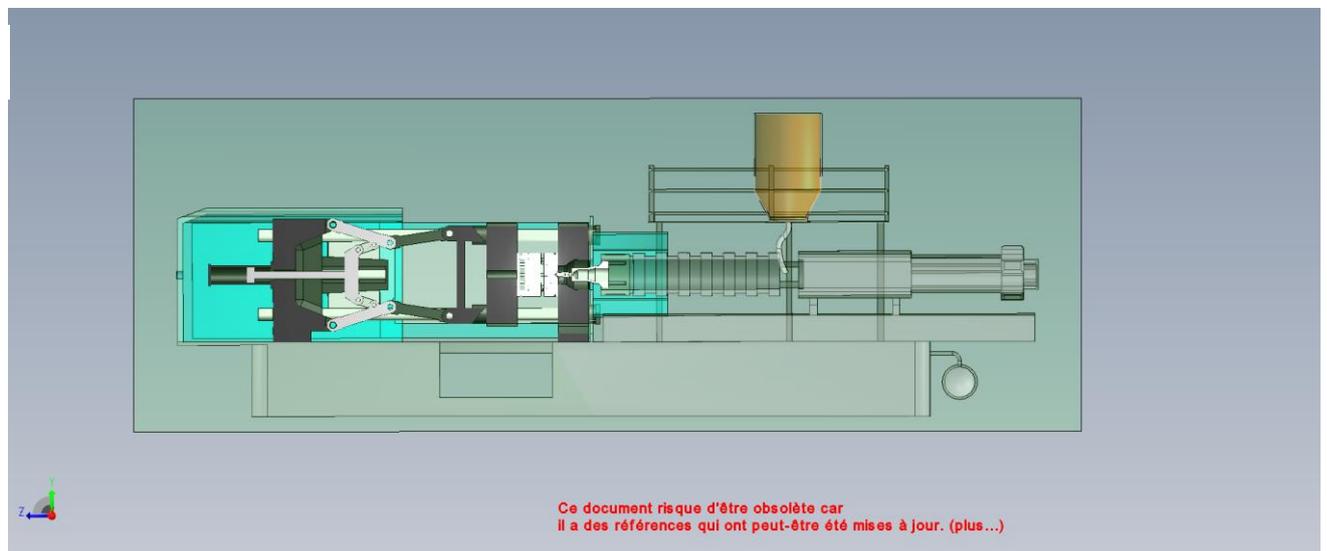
Machine presse d'injection plastique Horizontale 3D.
